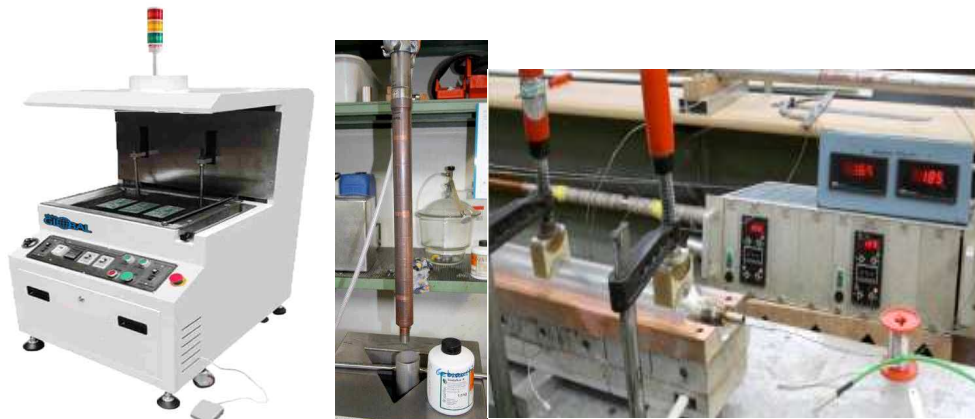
초전도 선재 Dip Solder 장비 및 부속품
